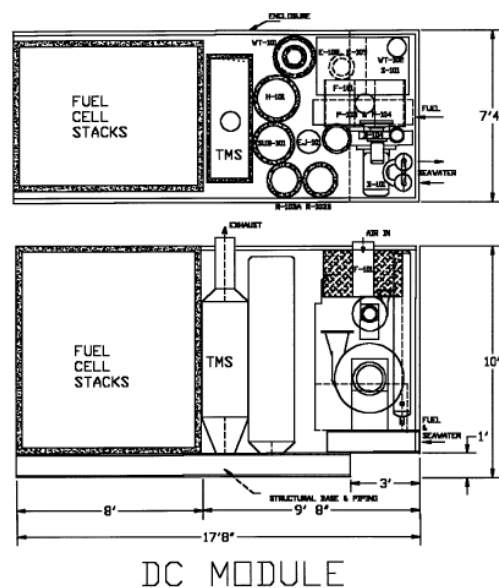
Planta y alzado del módulo MCFC (Karni and Fontneau, 1999).
